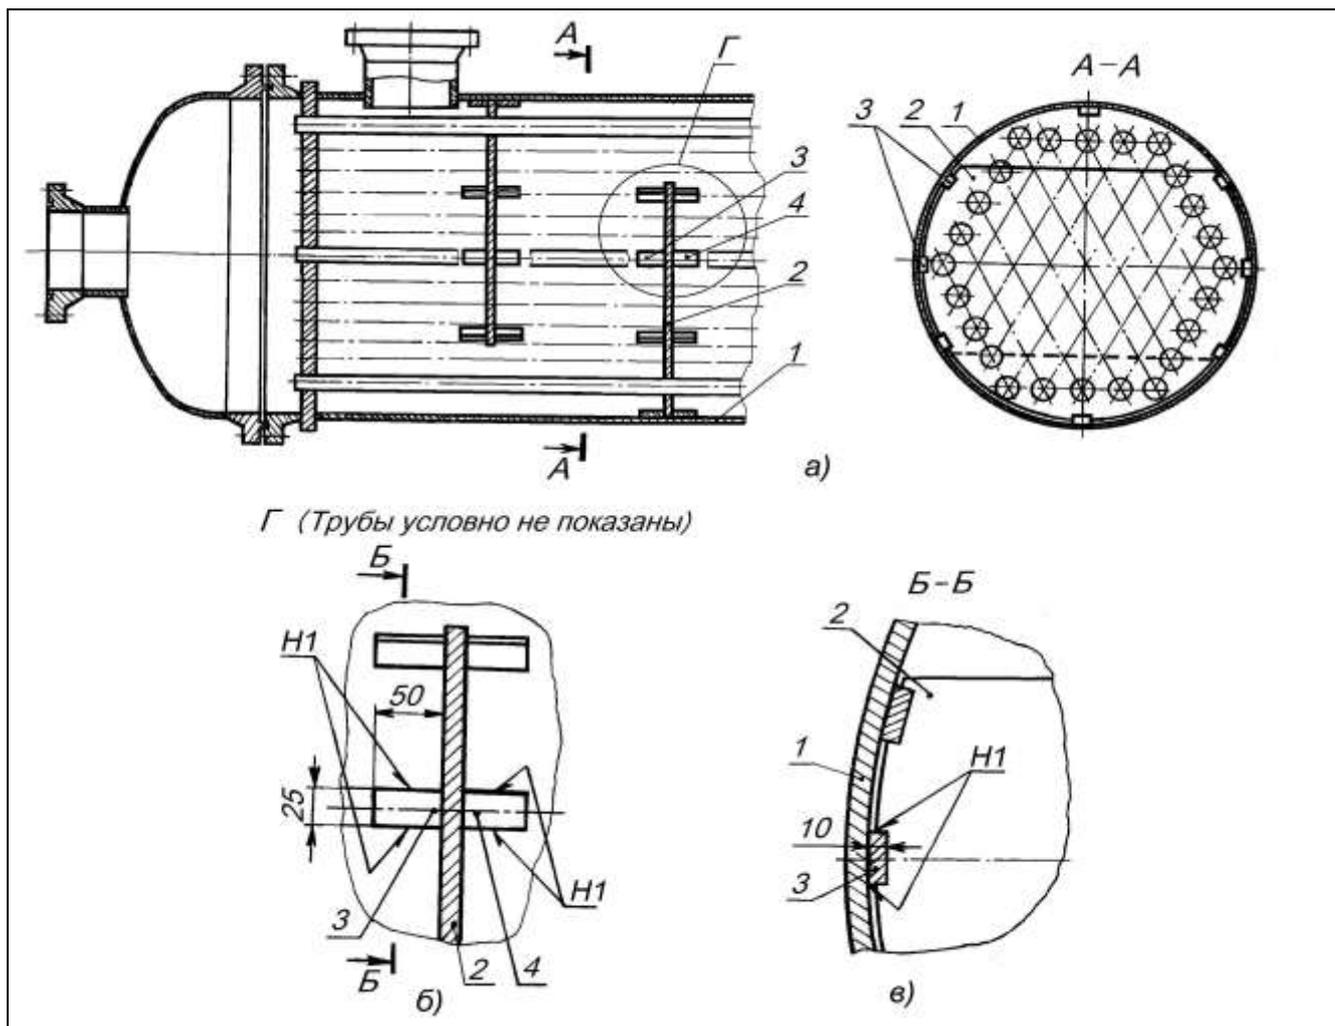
Схема крепления поперечных перегородок 2 к корпусу 1 с помощью приварных накладных пластин 3 и 4: а) – общий вид; б), в) – схемы приварки накладных пластин 3 и 4 к корпусу 1 аппарата нахлесточным сварным швом Н1
